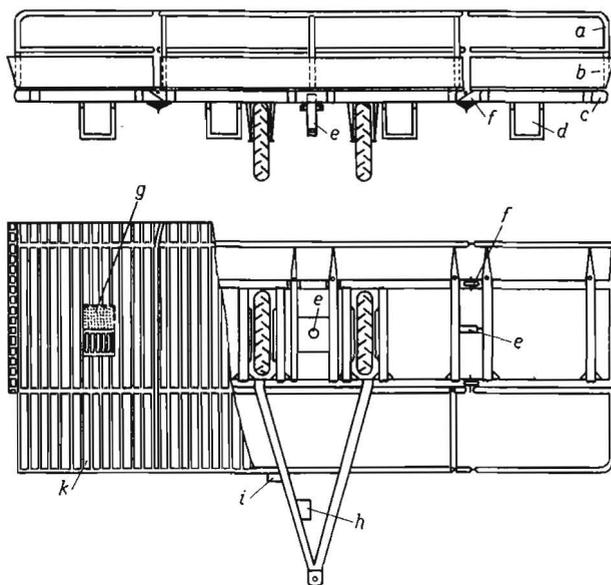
Erntewagen Typ „EH 64“; a Schutzgeländer, b Ernteplattform, c Rohrkonstruktion, d bewegl. Fußstützen, e Hydraulikzylinder, f Gelenk, g Sitz, h Hydraulikpumpe, i Hydraulikverteiler, k Kistenstapelfläche
